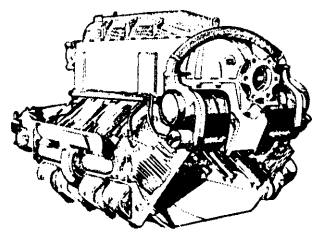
V-förmiger Motor hängend, luftgekühlt. Typ Argus As 10 c (Propellerseite)
